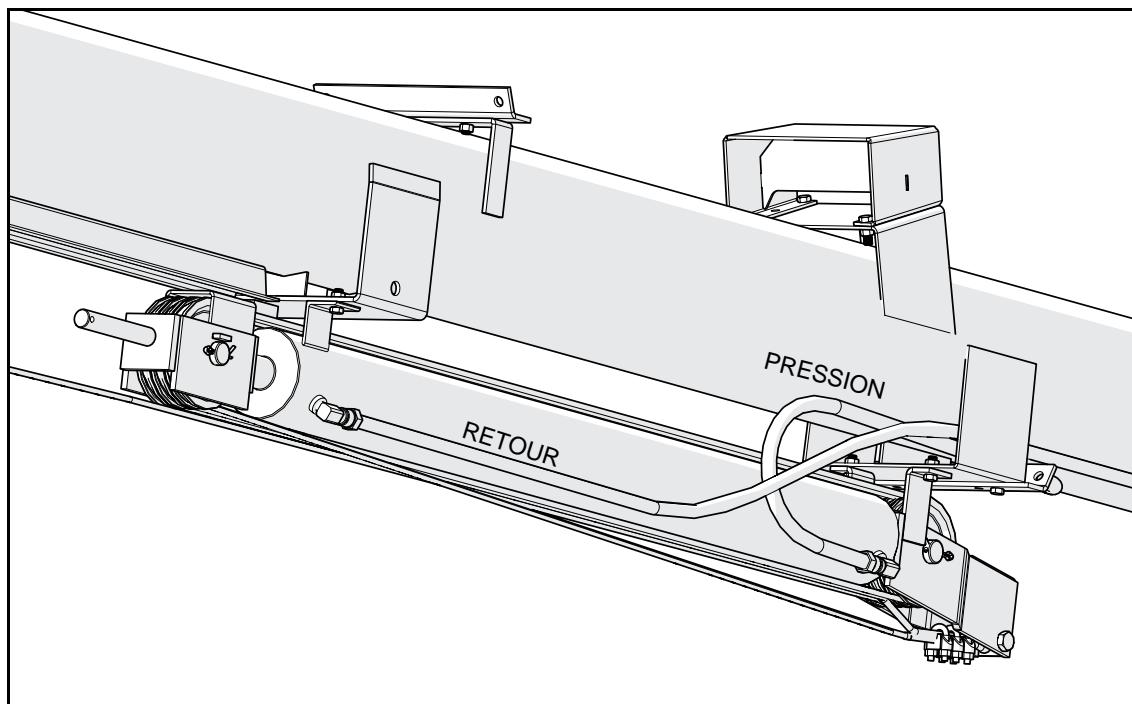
Raccords du cylindre du boyau hydraulique MKX100-83
